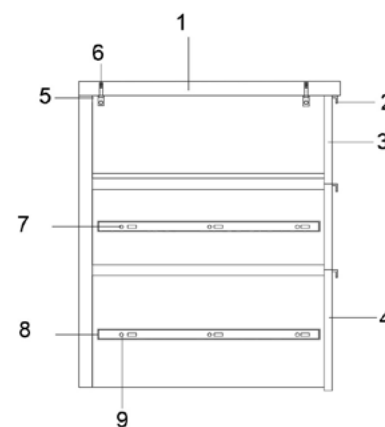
Detalle constructivo cajonera con mesón de acero inoxidable
